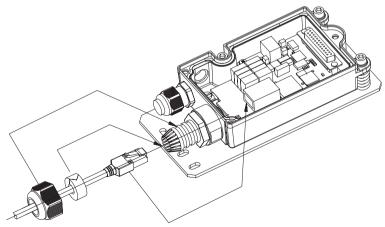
Montage Kabel mit RJ-45-Stecker
